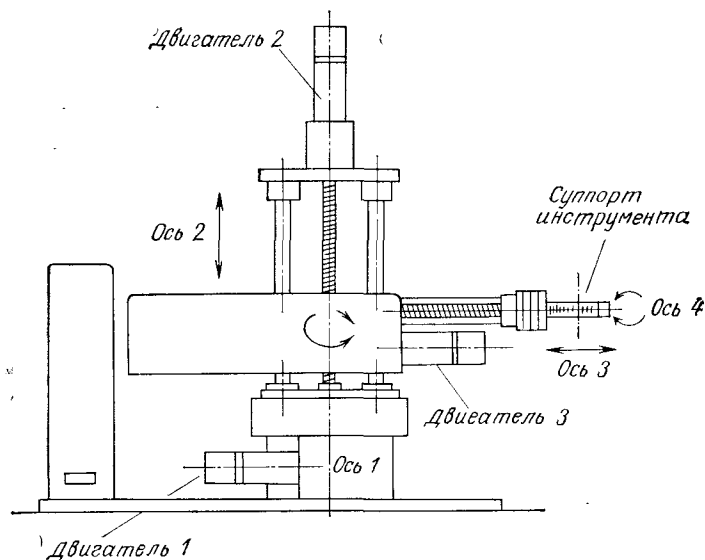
Схема конструкции SIROBOT 1. (Фирма SIEMENS.)
